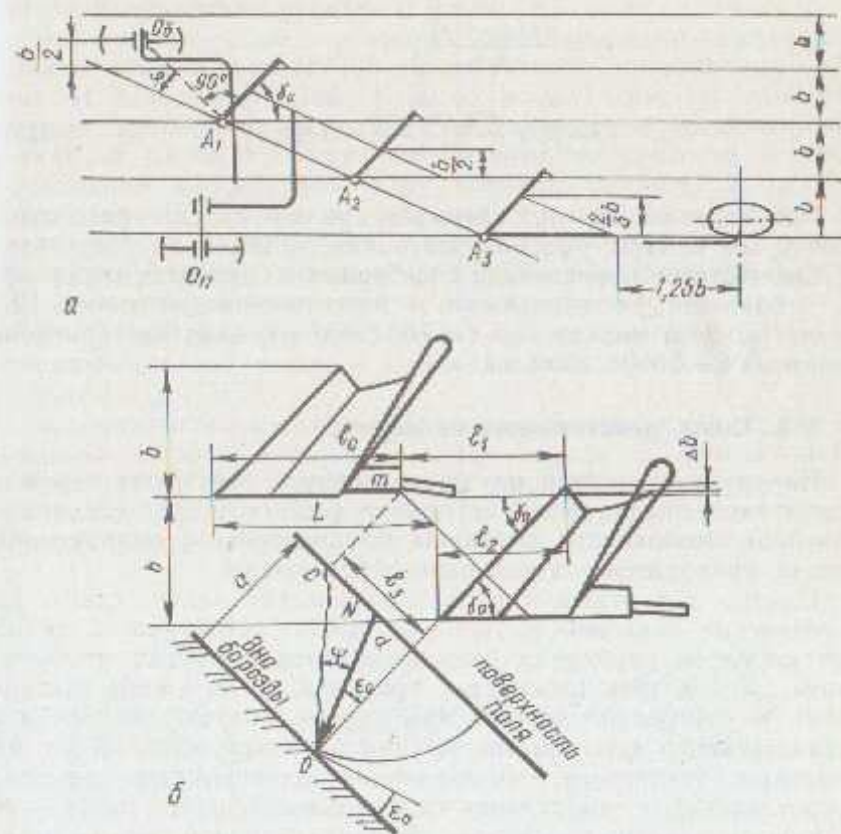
Размещение корпусов и колес плуга и определение расстояний между корпусами по ходу плуга:
